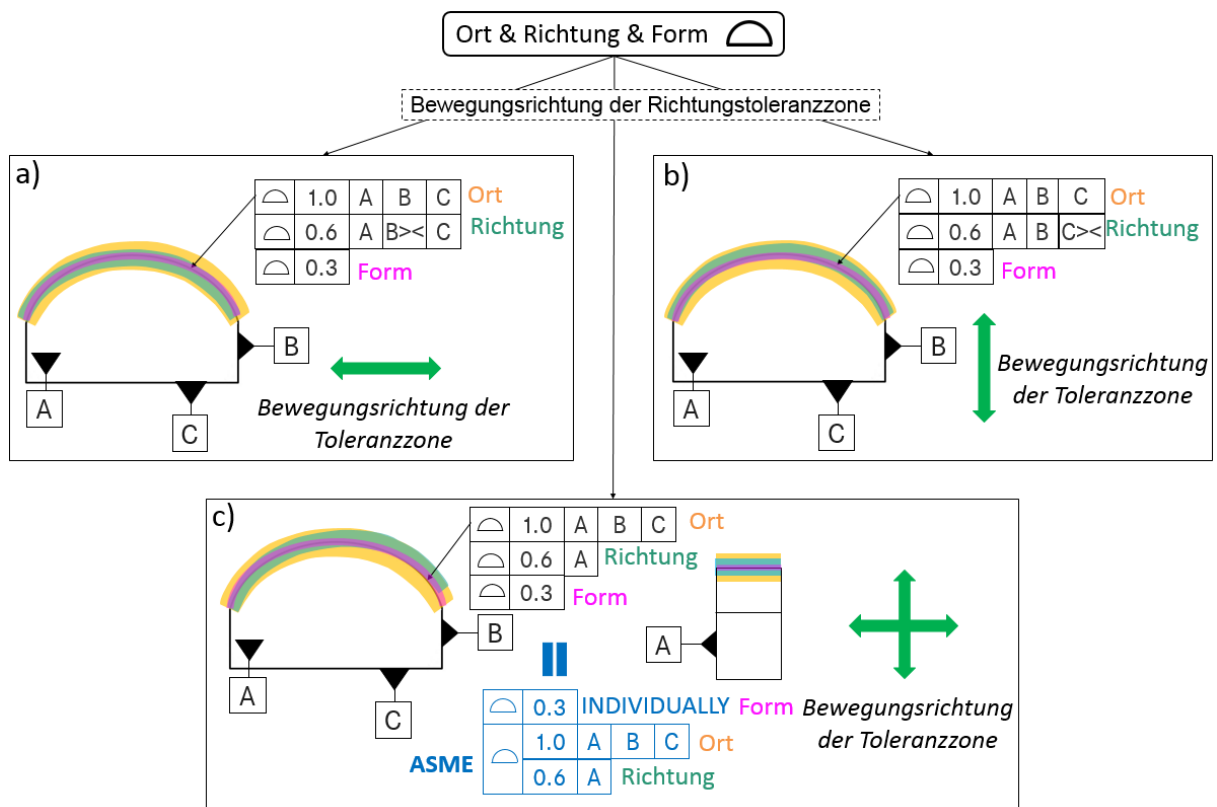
Verbundtoleranz der Flächenprofilltoleranz: Ort, Richtung und Form
